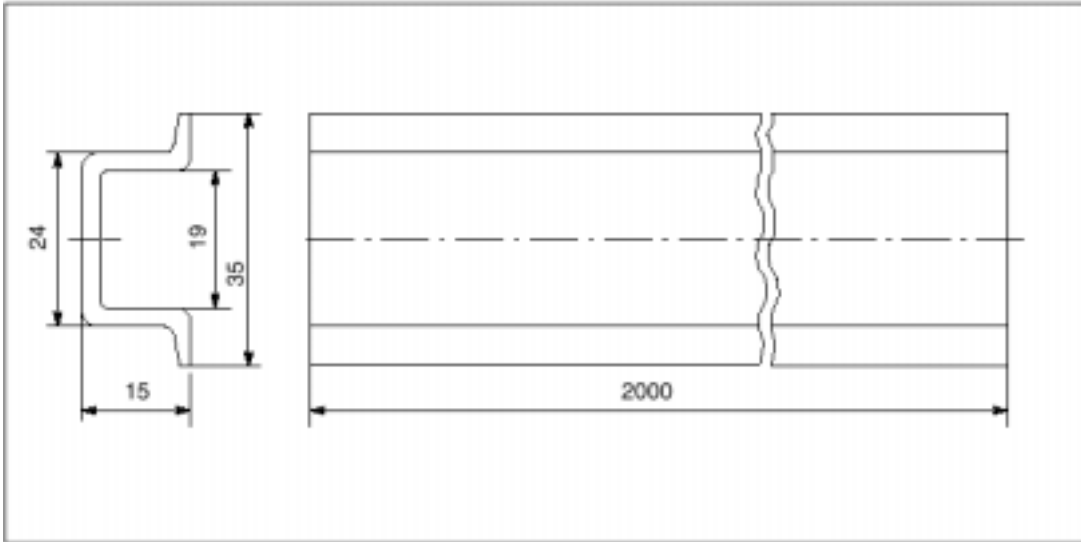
Чертеж с размерами 2000-миллиметровой стандартной профильной шины
